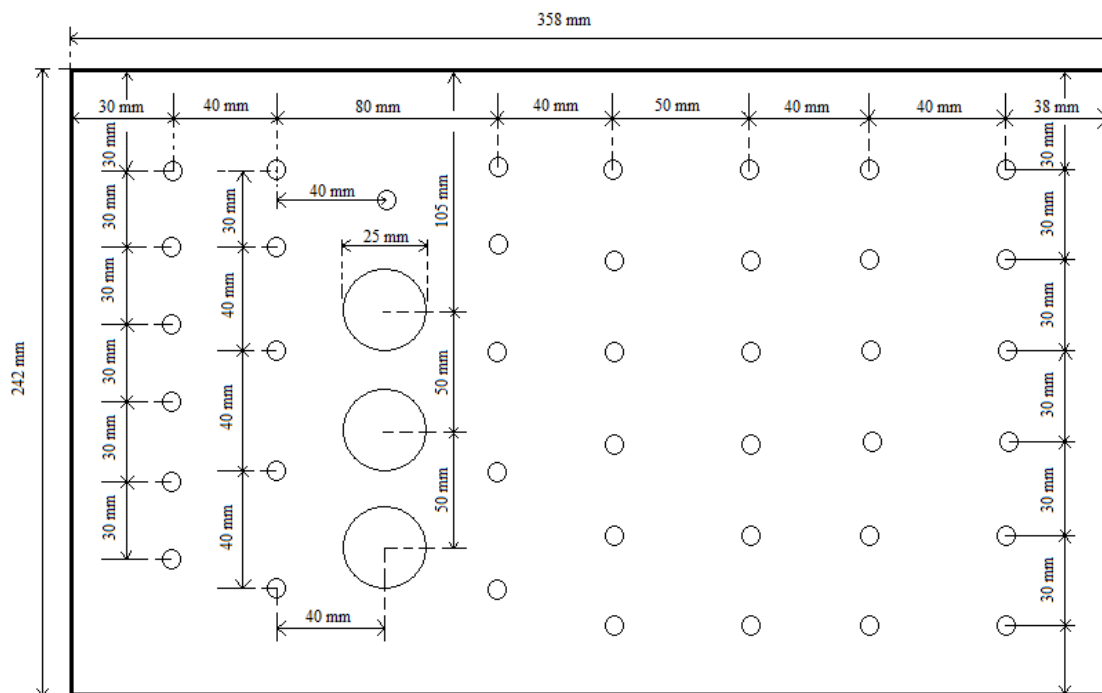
medidas do painel com a posição dos furos, (desenho fora de escala). Fonte: O autor.
